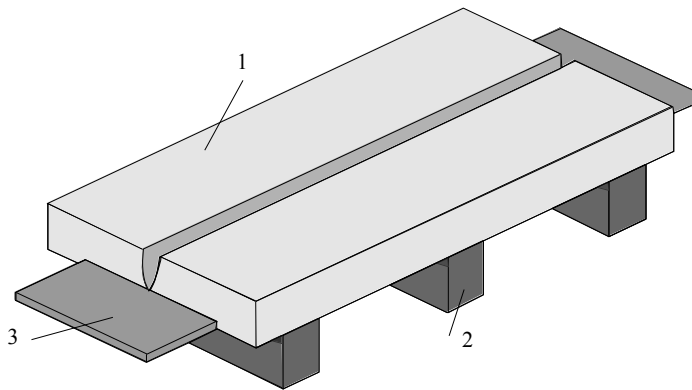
Стиконе з'єднання роторної сталі 25Х2НМФА де 1- пластина; 2- ребро жорсткості; 3 – вивідна планка.
